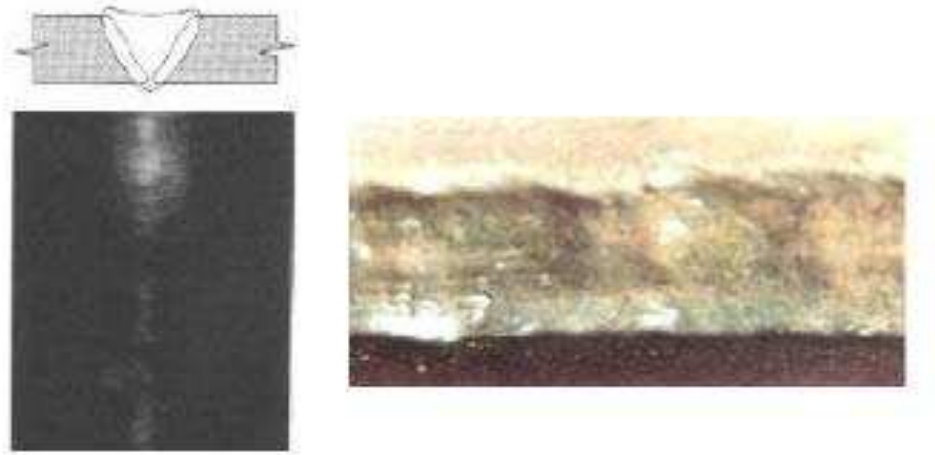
Concavidad externa o falta de relleno en soldadura.
